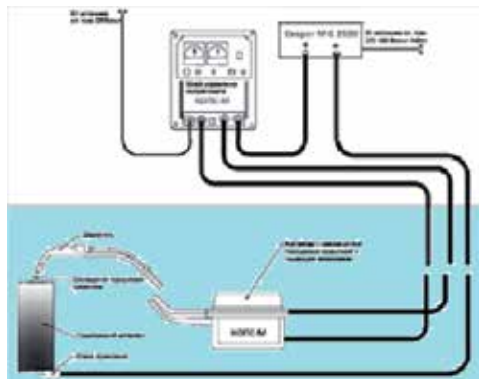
Принципиальная схема осуществления процесса сварки на стенде.
